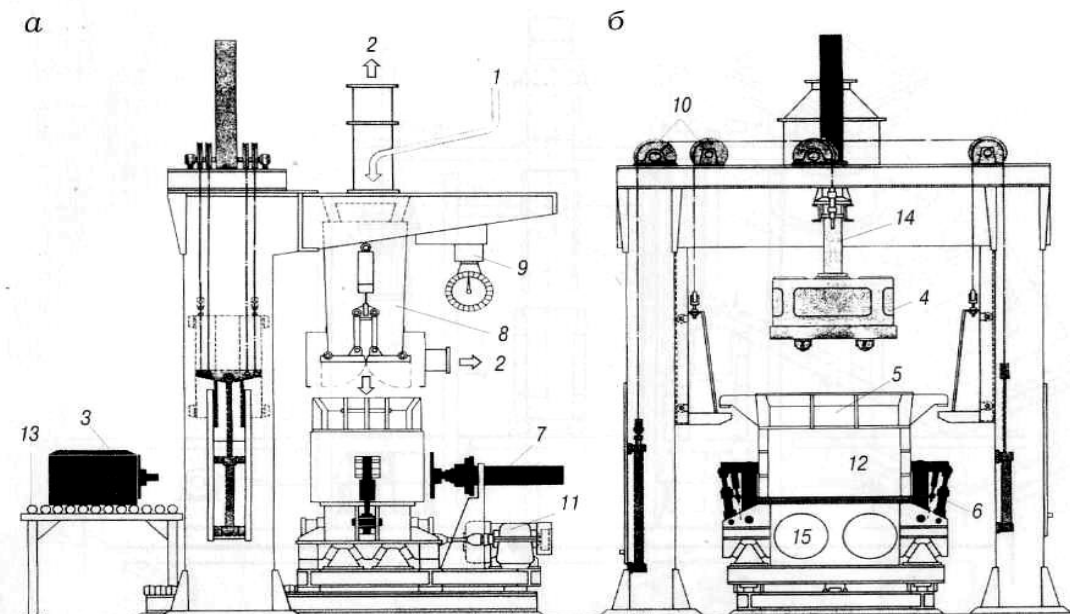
Вибромашина стационарного типа с одним вибростолом и монолитной виброформой: 1-подача шихты; 2- газоотсос и вакуумирование; 3-готовый зеленый анод; 4- пригруз с формовочной плитой; 5-виброформа; 6- захват виброформы; 7-толкатель; 8-взвешивающий кубель; 9-автоматическая взвешивающая система; 10-механизм привода пригруза; 11- привод вибростола; 12- вибростол; 13- рольганд; 14-шток пригруза; 15 – дебалансы.
